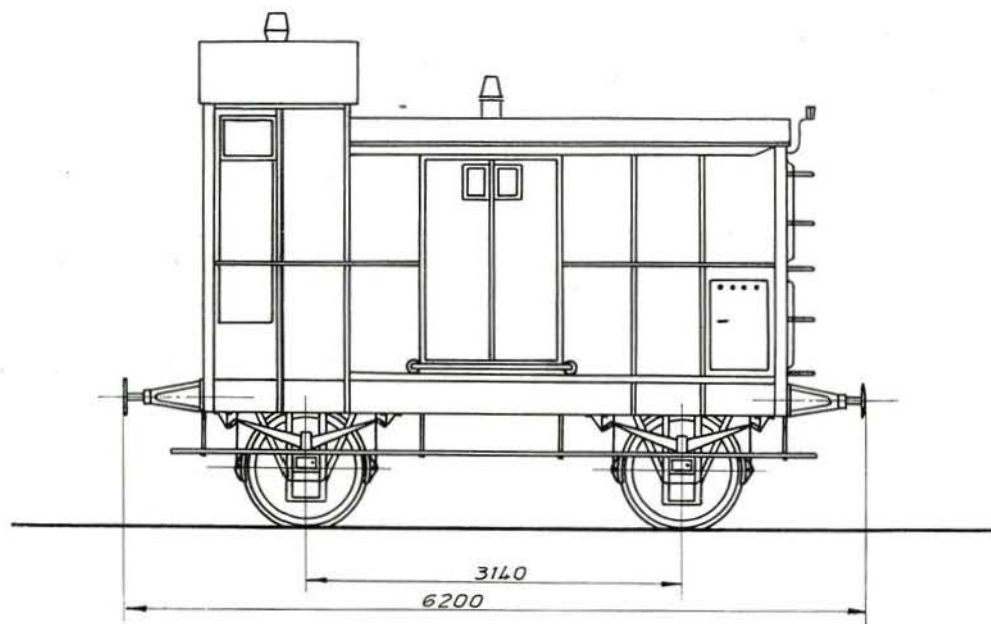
Pw Länderbauart Preußen, Baujahr 1865
